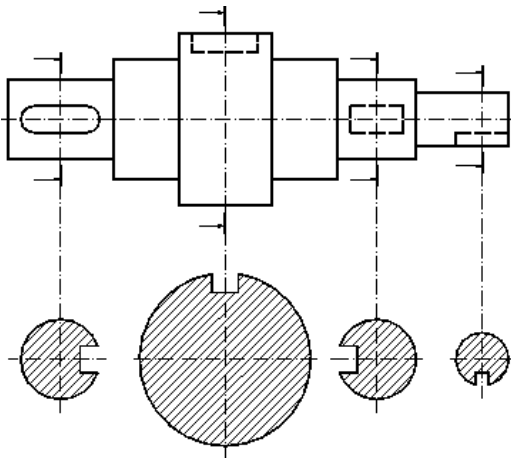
Desplazamiento de sección lo largo del plano de corte.
